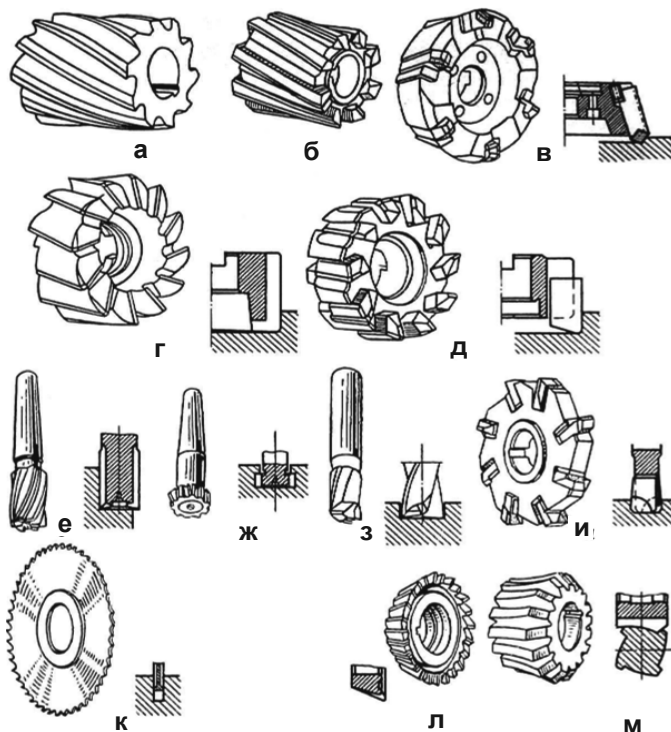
Типи фрез: а, б – циліндричні; в, г, д – торцеві; е, ж – кінцеві; з – шпонкові; и – дискові; к – відрізні та прорізні; л – кутові; м – фасонні
